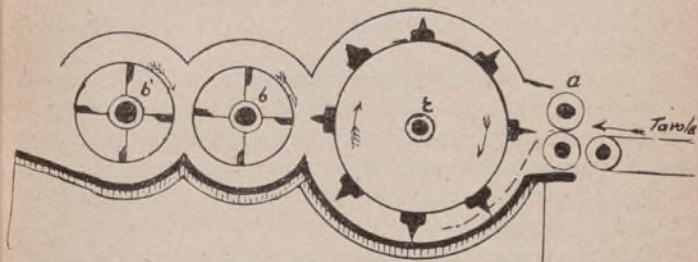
Schema di apritrice; r tamburo a spine, bb' tamburi di sbattimento.
